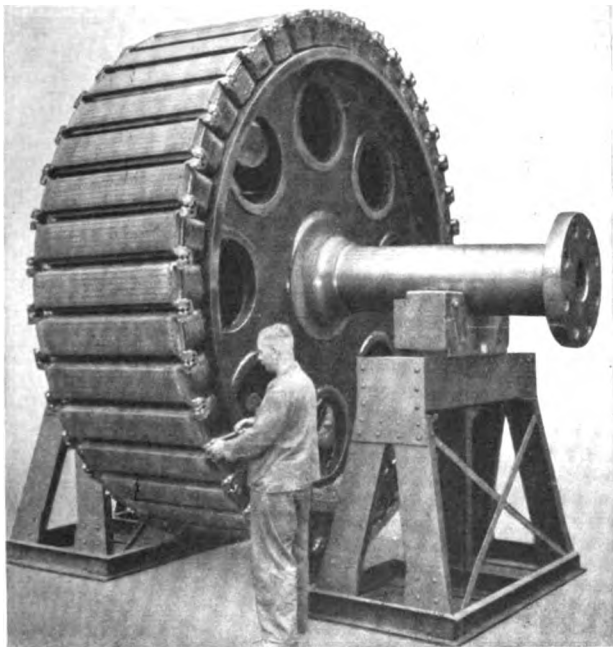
Schiffsschraubenmotor, Polrad fertig zum Einbau.
